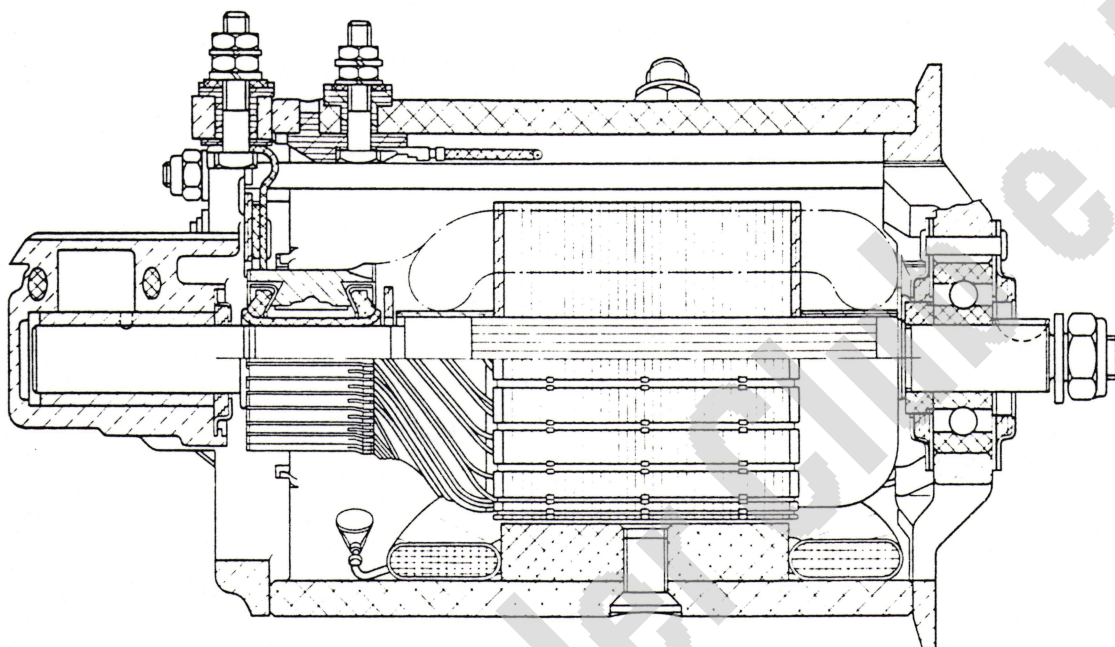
Längsschnitt durch die Lichtmaschine.
